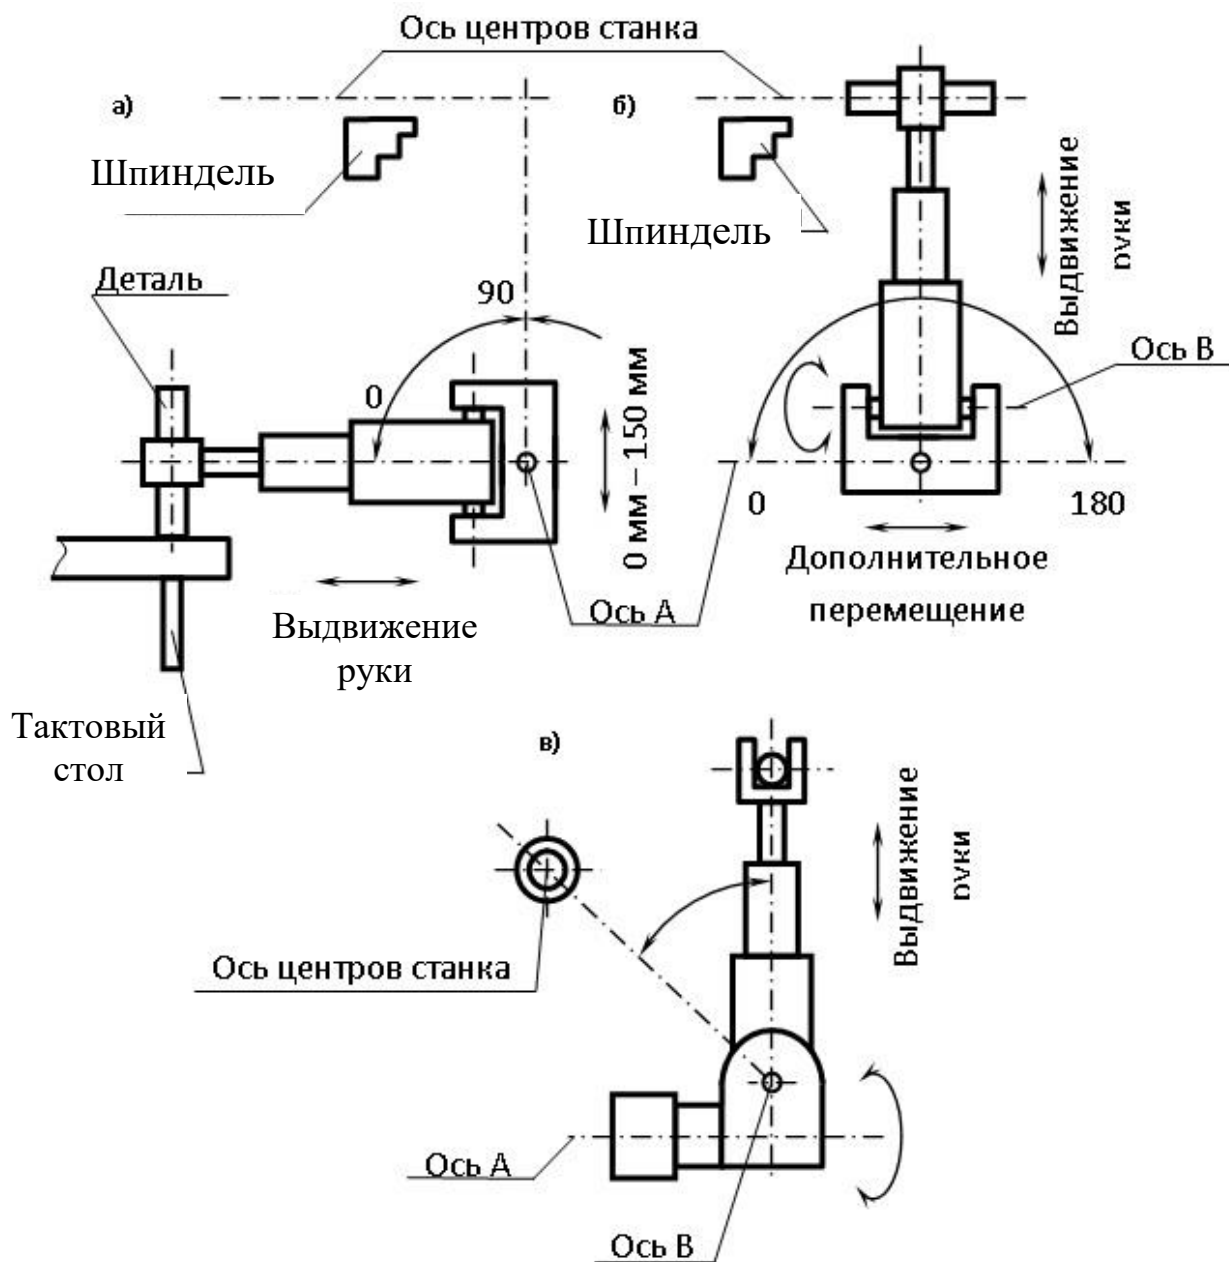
Схема автоматической обрабатывающей ячейки:
